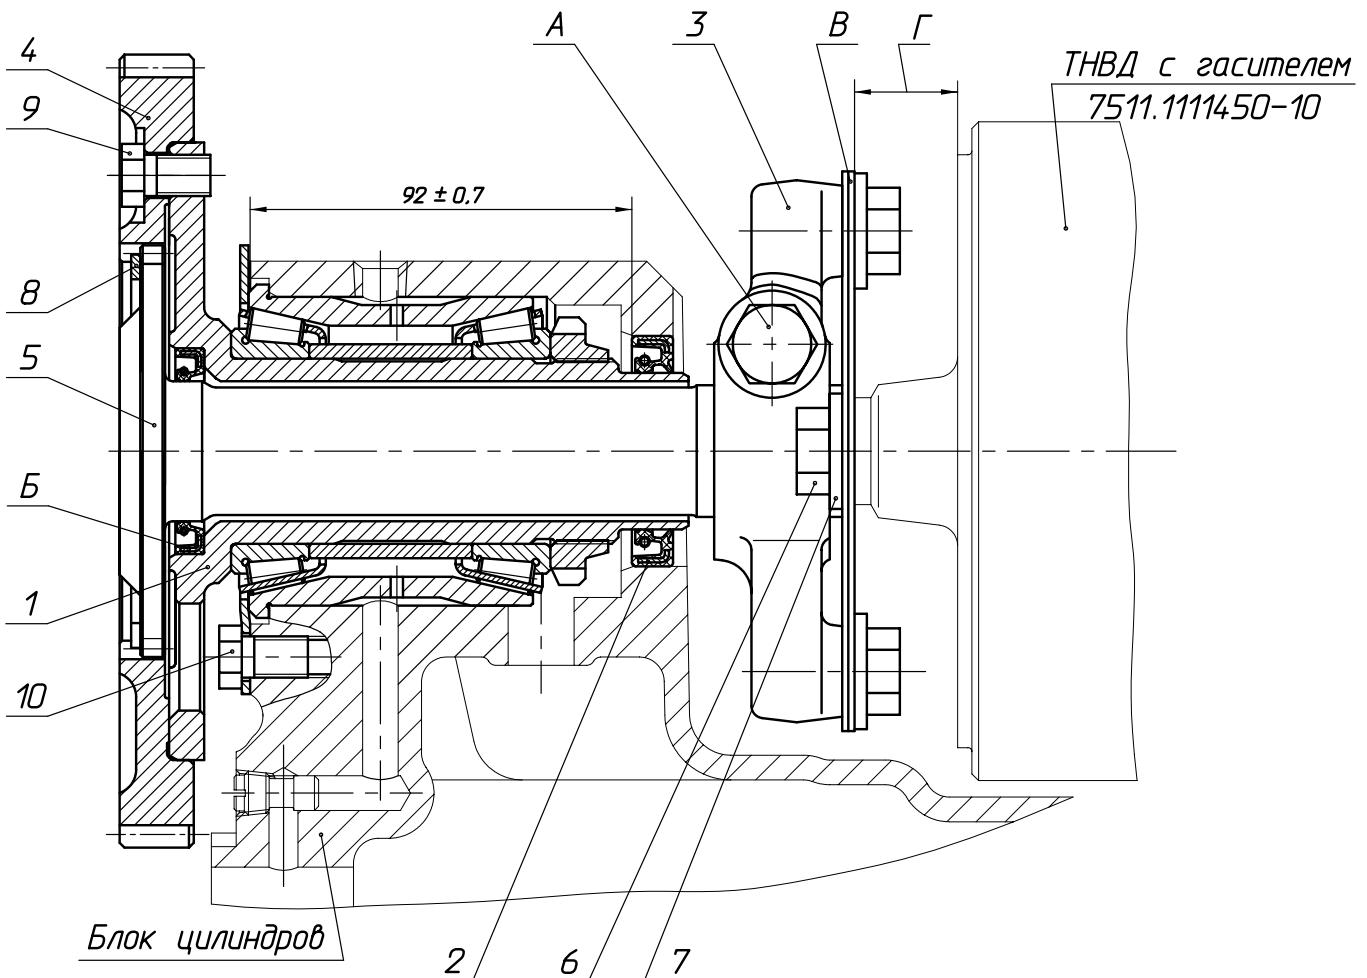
Установка привода ТНВД, 7511.1029002-01
